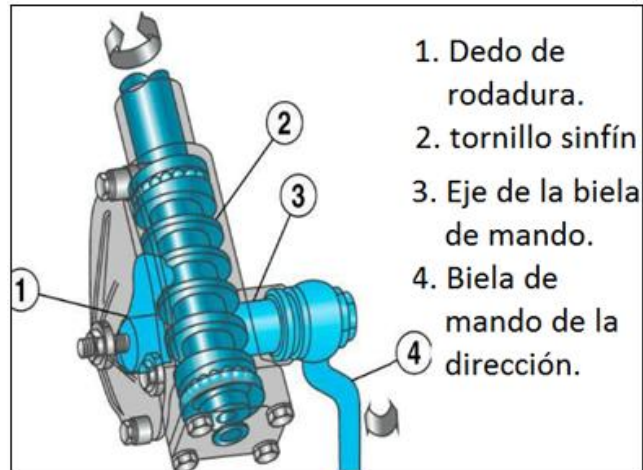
Mecanismo de dirección por tornillos sinfín cilíndrico y dedo de rodadura
